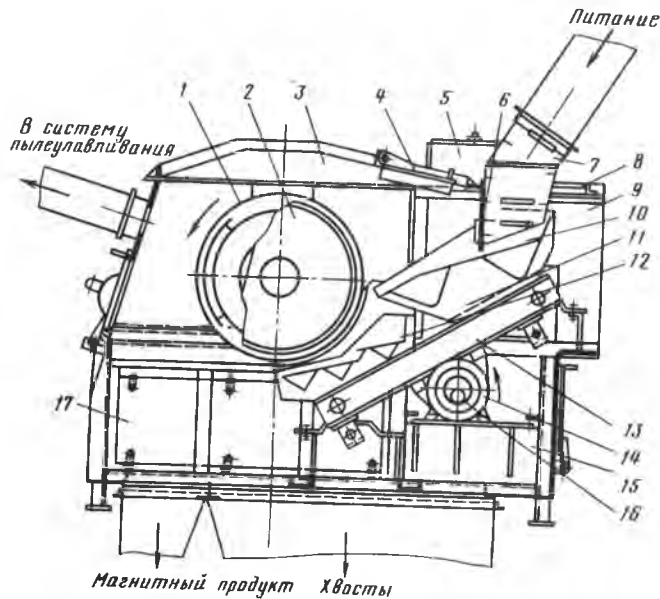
Электромагнитный барабанный сепаратор ЭБС-80/170: 1 – барабан; 2 – электромагнитная система; 3 – крышка; 4, 17 – люки; 5 – маслобак; 6 – шибер; 7 – бункер; 8 – крышка; 9 – корпус; 10 – верхний лоток; 11 – вибропитатель; 12 – нижний лоток; 13 – рама; 14 – электродвигатель; 15 – кронштейн; 16 – вибровозбудитель
